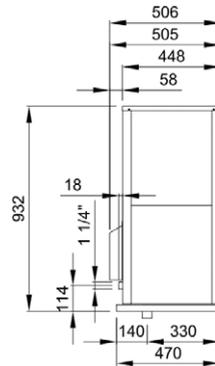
Außenabmessungen der Wärmepumpe Seitenansicht
